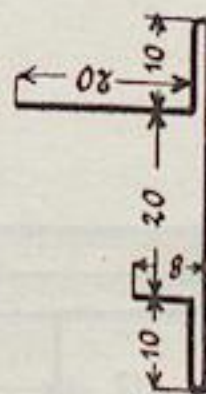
Querschnitt der eingeschobenen Blechnute.
